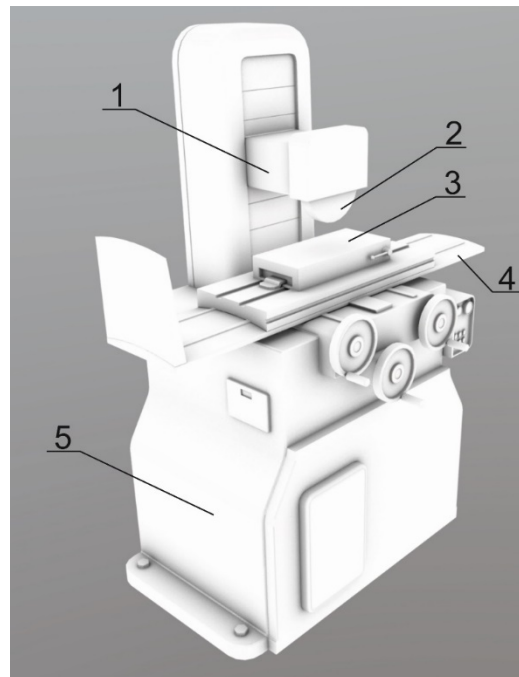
3D-модель плоско-шліфувального верстата: 1 – шпindelний вузол; 2 – інструмент-диск; 3 – магнітна плита; 4 – стіл; 5 – станина
